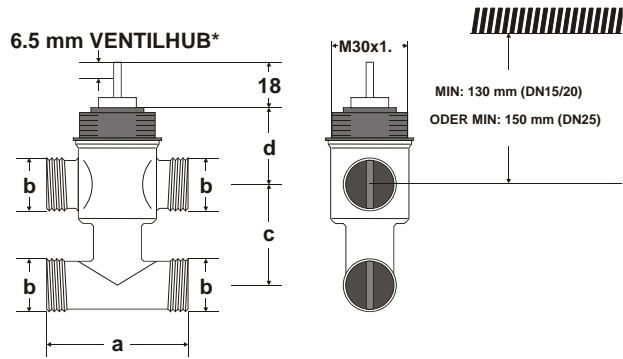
Dreiwegeventile mit Bypass, Abmessungen
